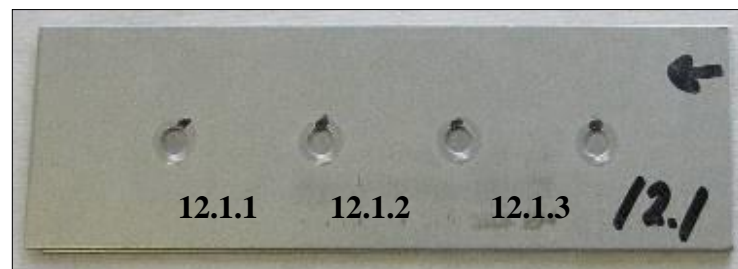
Внешний вид точечной контактной сварки образца № 12.1
